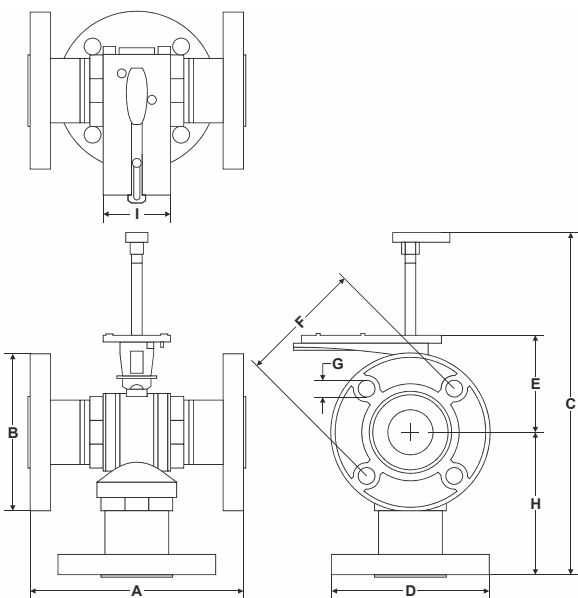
3-Wege-Ventile DN 50 / 65 Abmessungen
